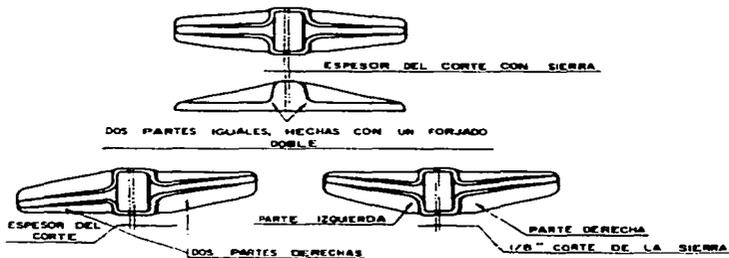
El forjado doble puede ser más económico cuando la pieza es simétrica, las dos partes derechas o una parte derecha y otra izquierda
